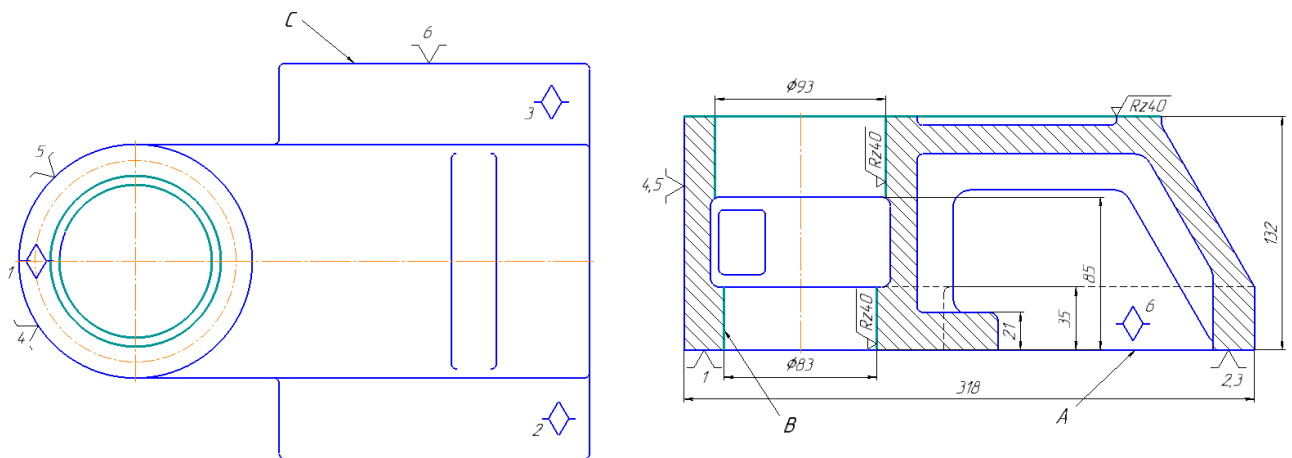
Схема базування та закріплення заготовки на операції 015
